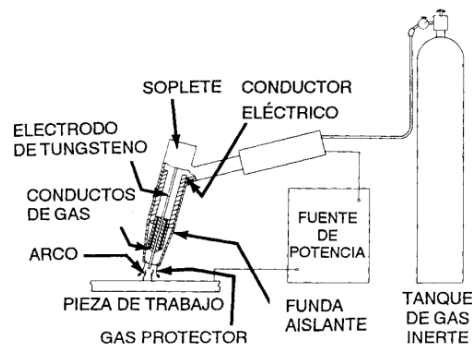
Equipo de soldadura GTAW [31]
